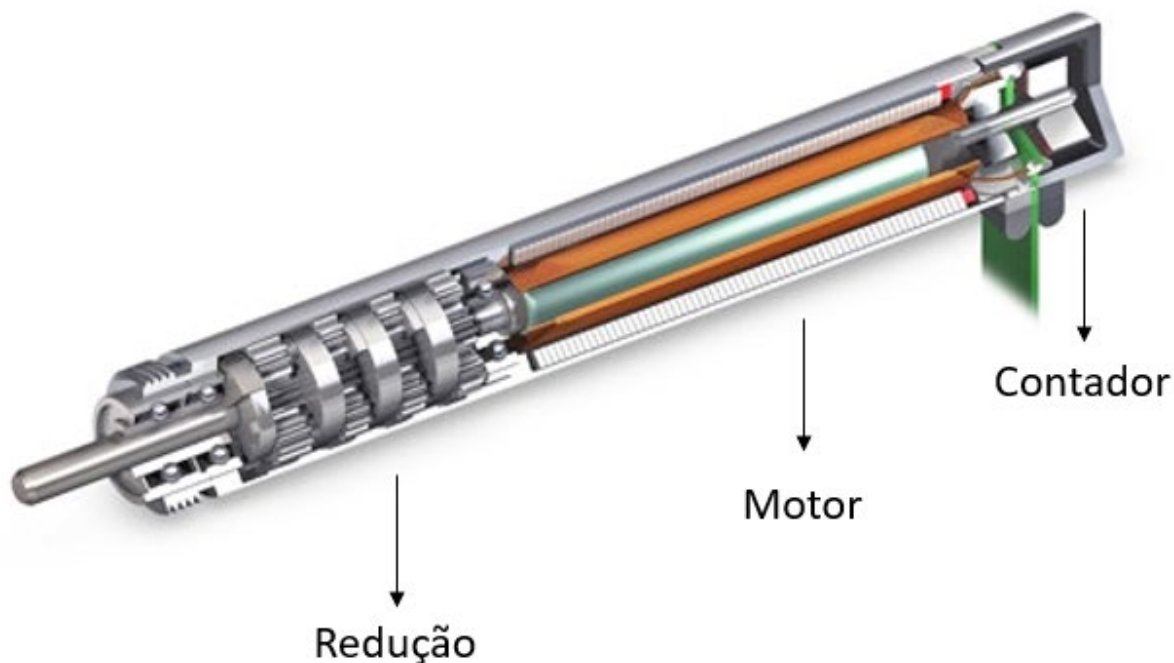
Motor Elétrico com Redução e *Encoder*. Modificado (Maxon)
